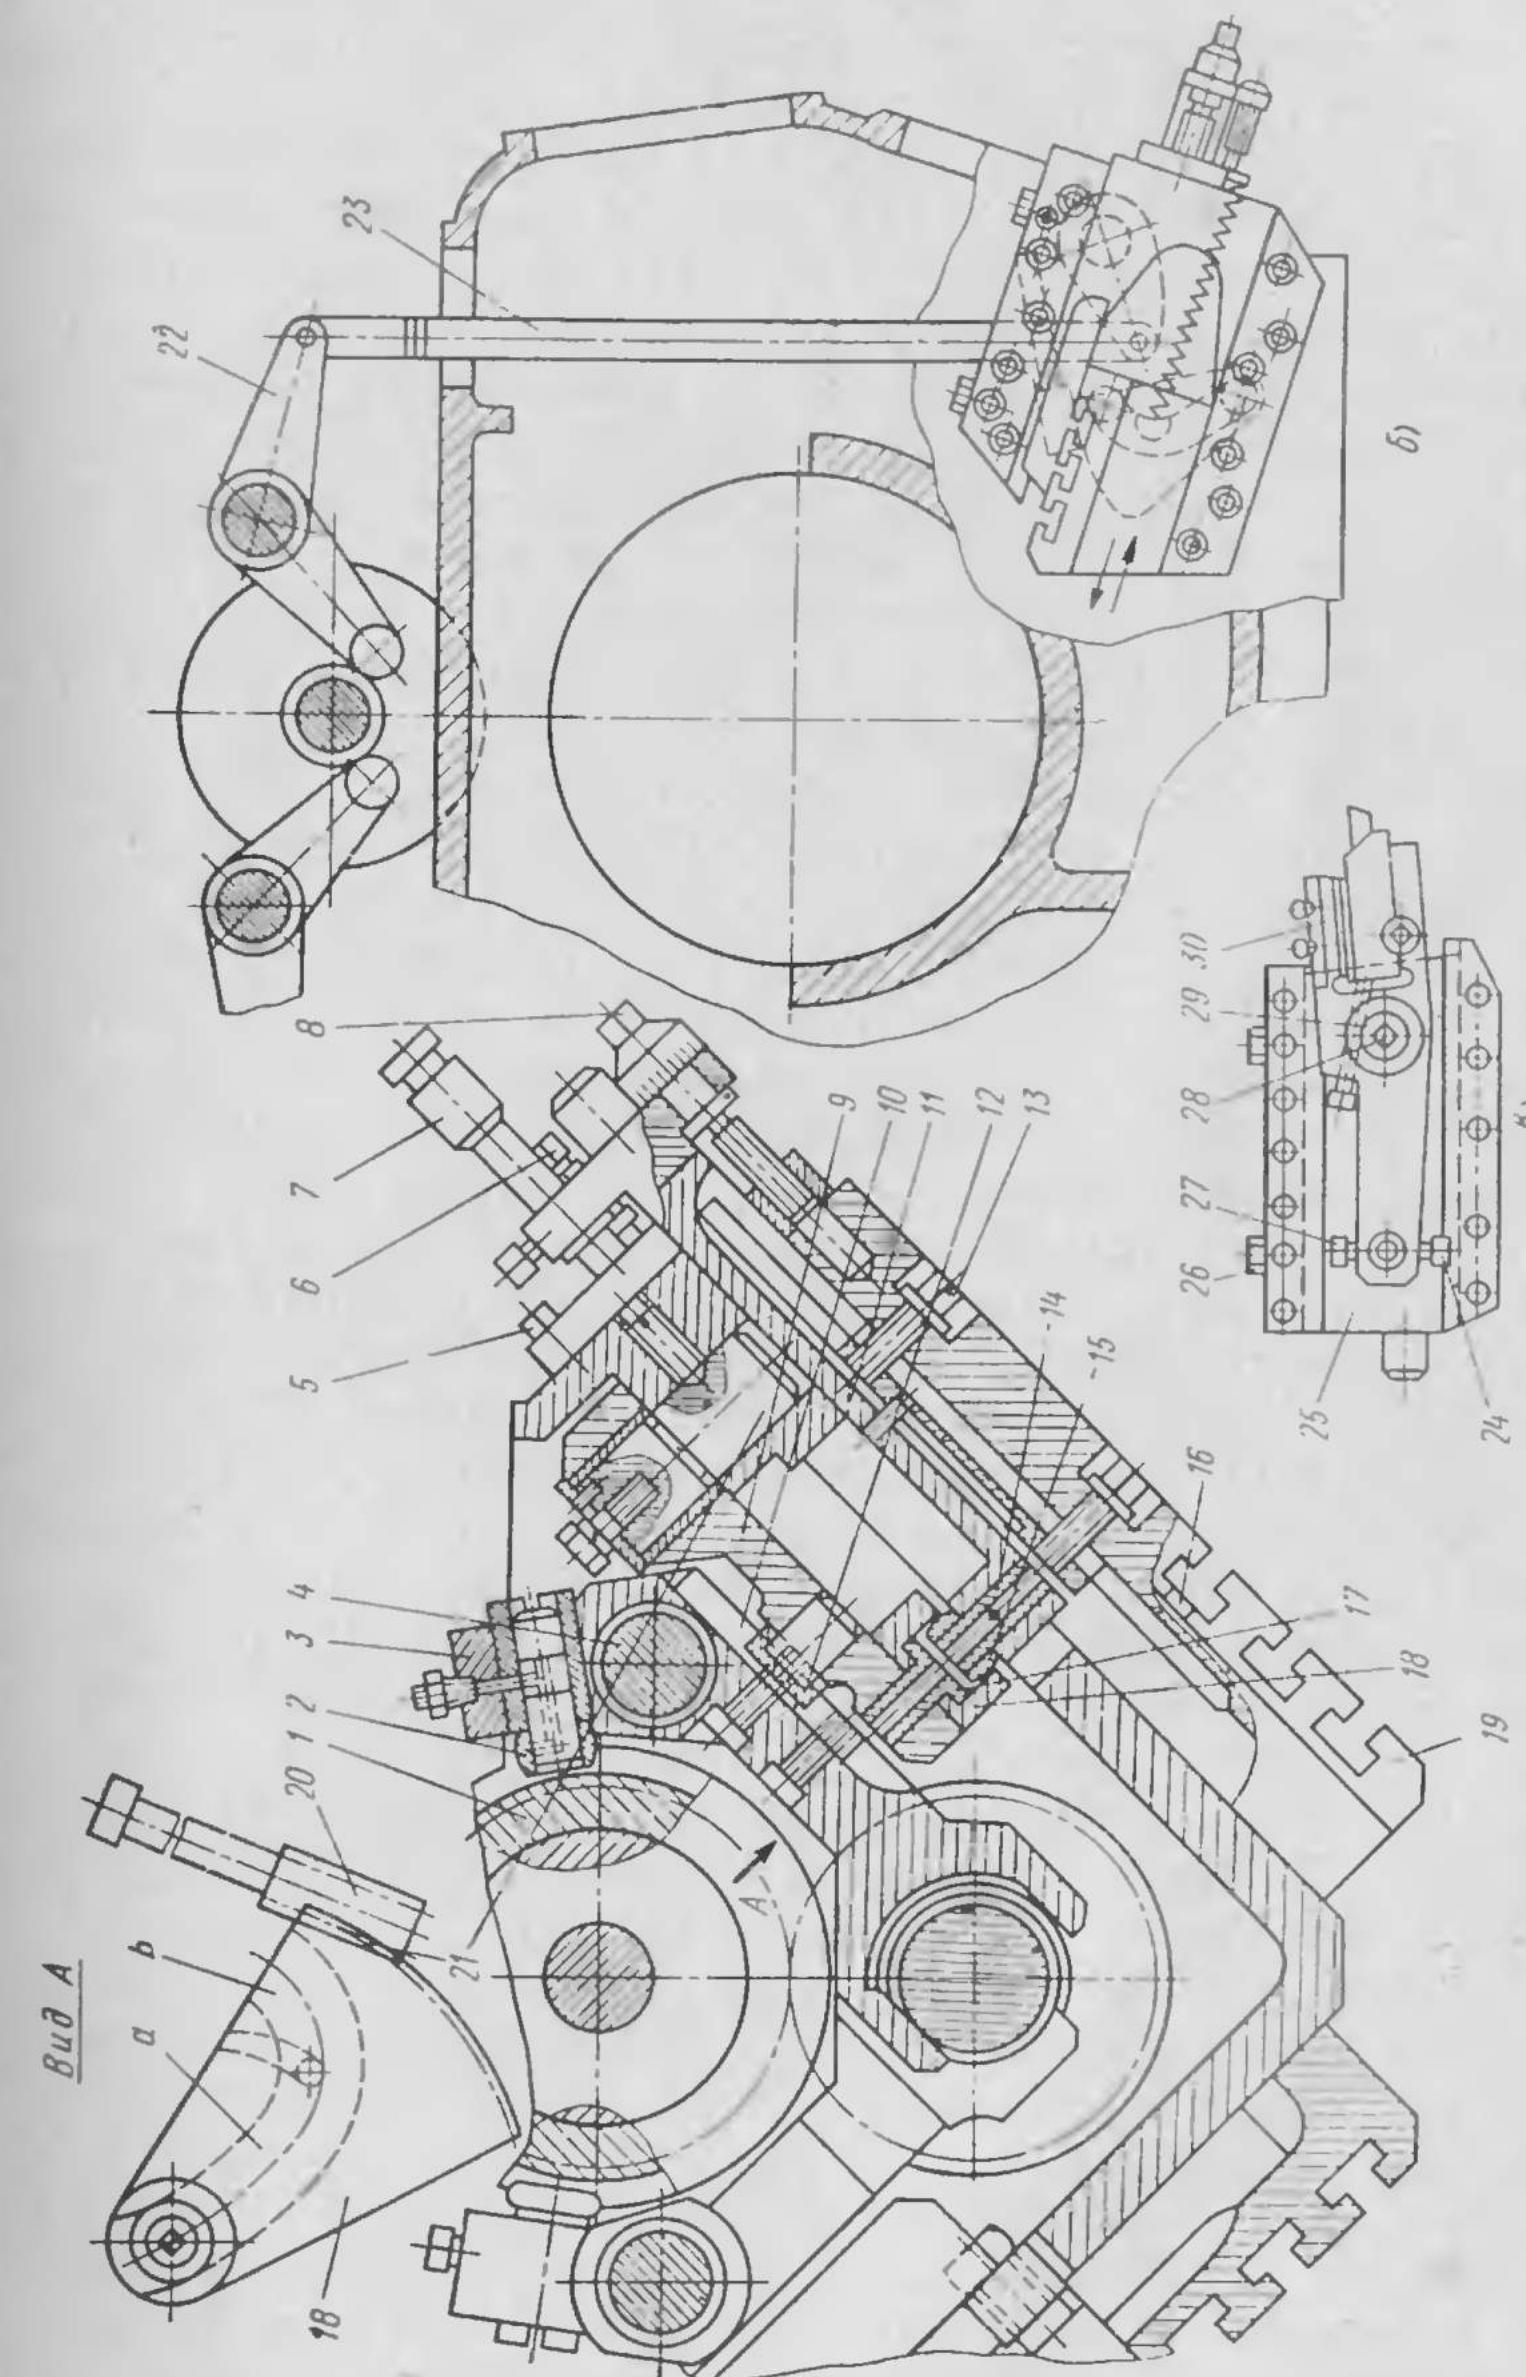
Верхний задний поперечный суппорт (а), привод заднего нижнего суппорта (б) и отрезной суппорт (в) автомата
